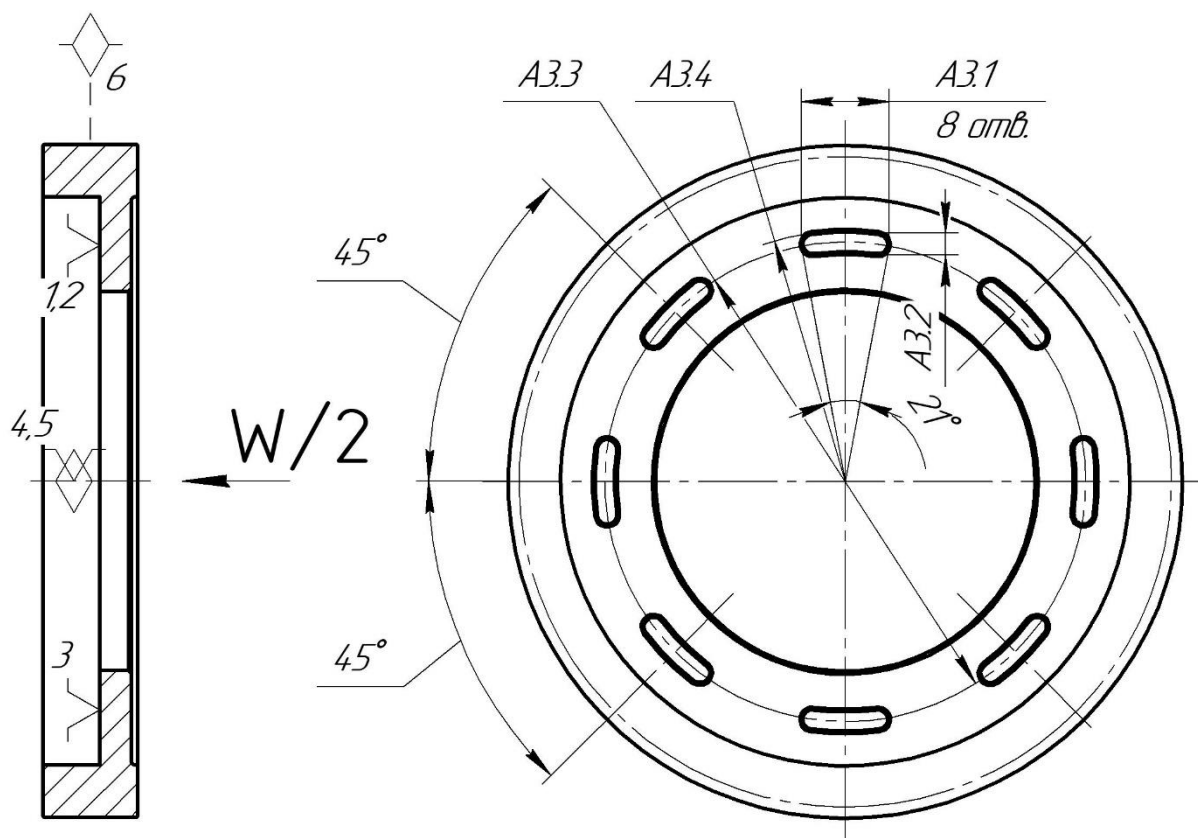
Принципиальная схема зажима заготовки в приспособлении с указанием мест приложения силы зажима.
